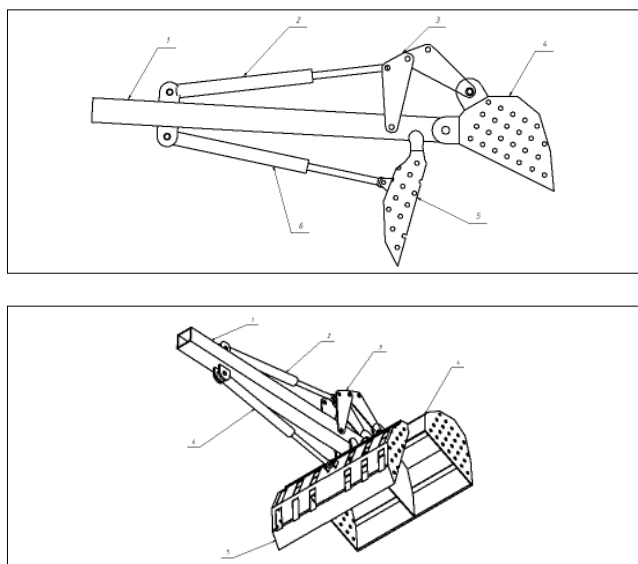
Уширенный ковш с дополнительным захватом: 1 – рукоять; 2 – гидроцилиндр поворота ковша; 3 – толкатели; 4 – ковш; 5 – захват; 6 – гидроцилиндр поворота захвата
